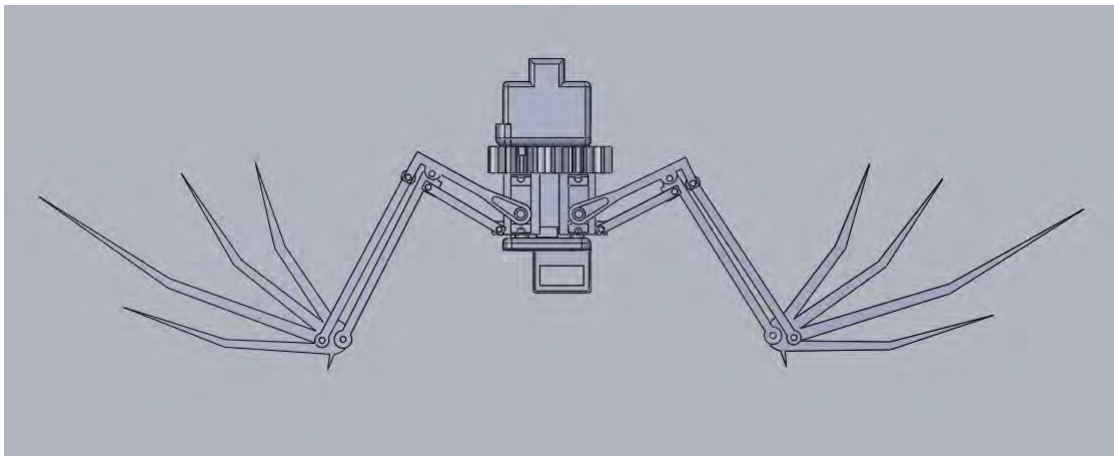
Vista superior del ensamblaje en SolidWorks.
